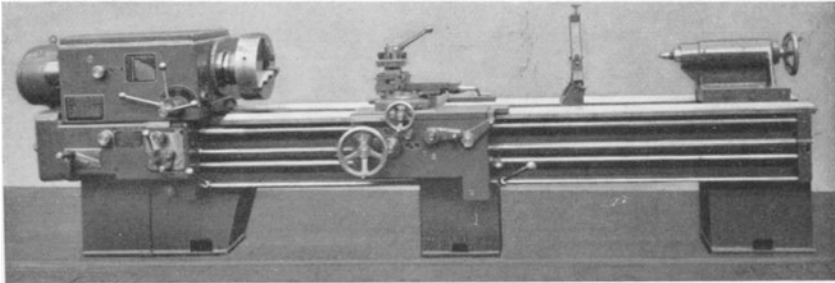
Geschweißte Leitspindeldrehbank.
